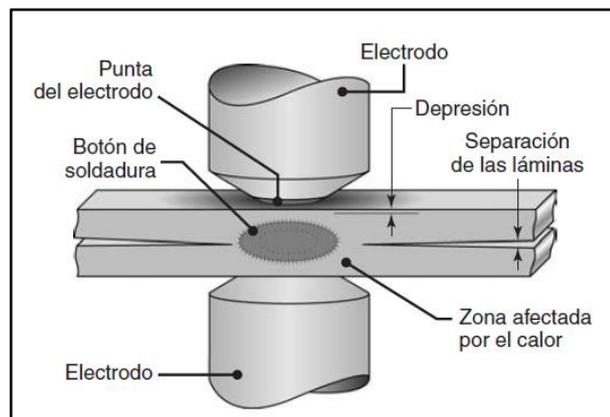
Sección transversal de un punto de soldadura mostrando el botón de soldadura.
